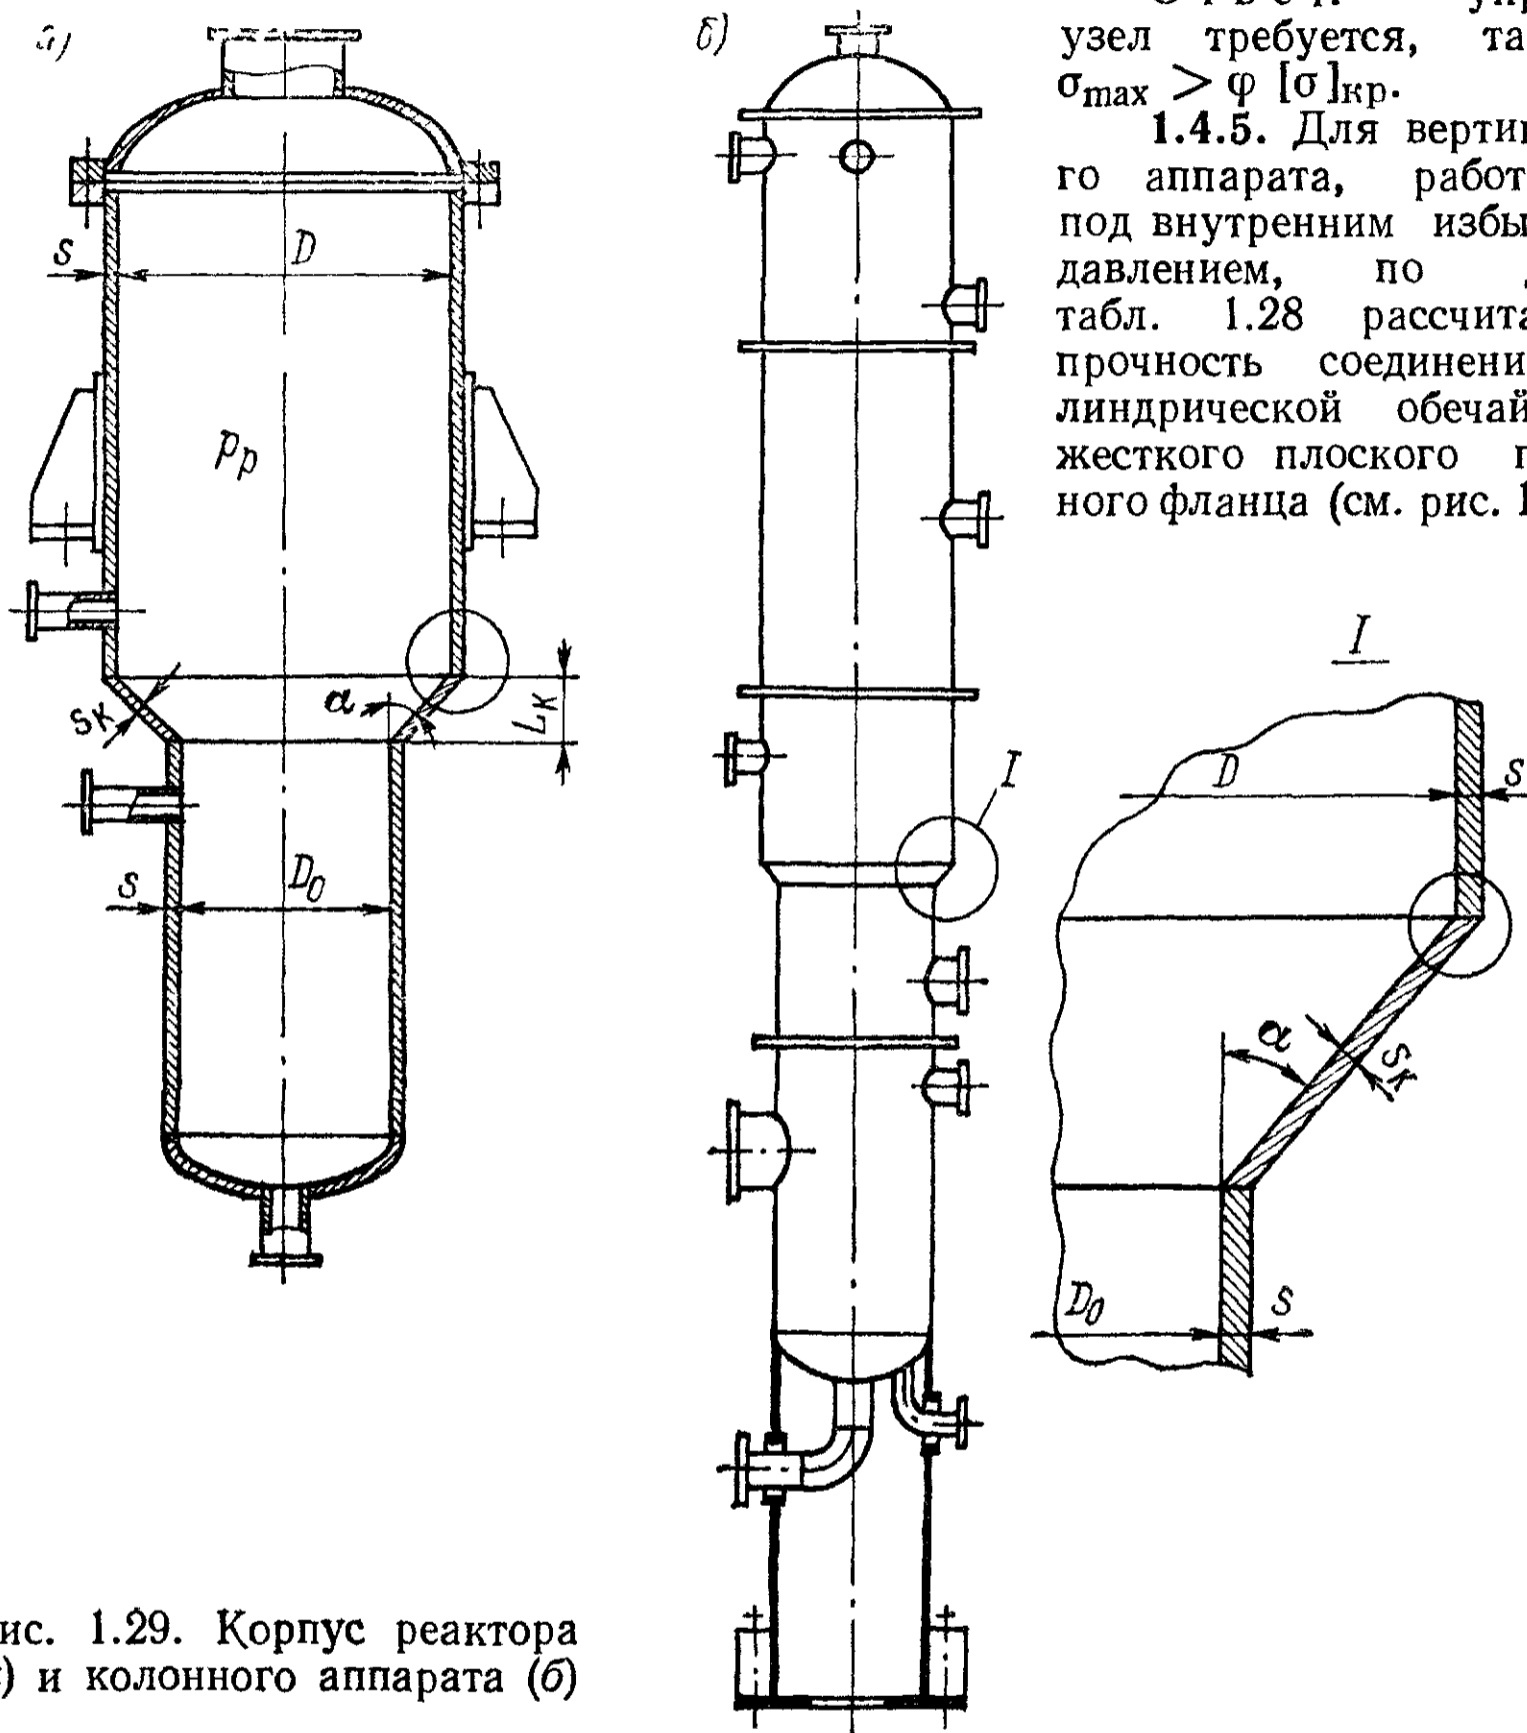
Корпус реактора (а) и колонного аппарата (б)
